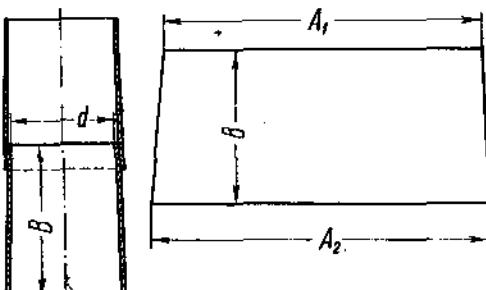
Приближенный способ построения развернутой боковой поверхности усеченного конуса.
